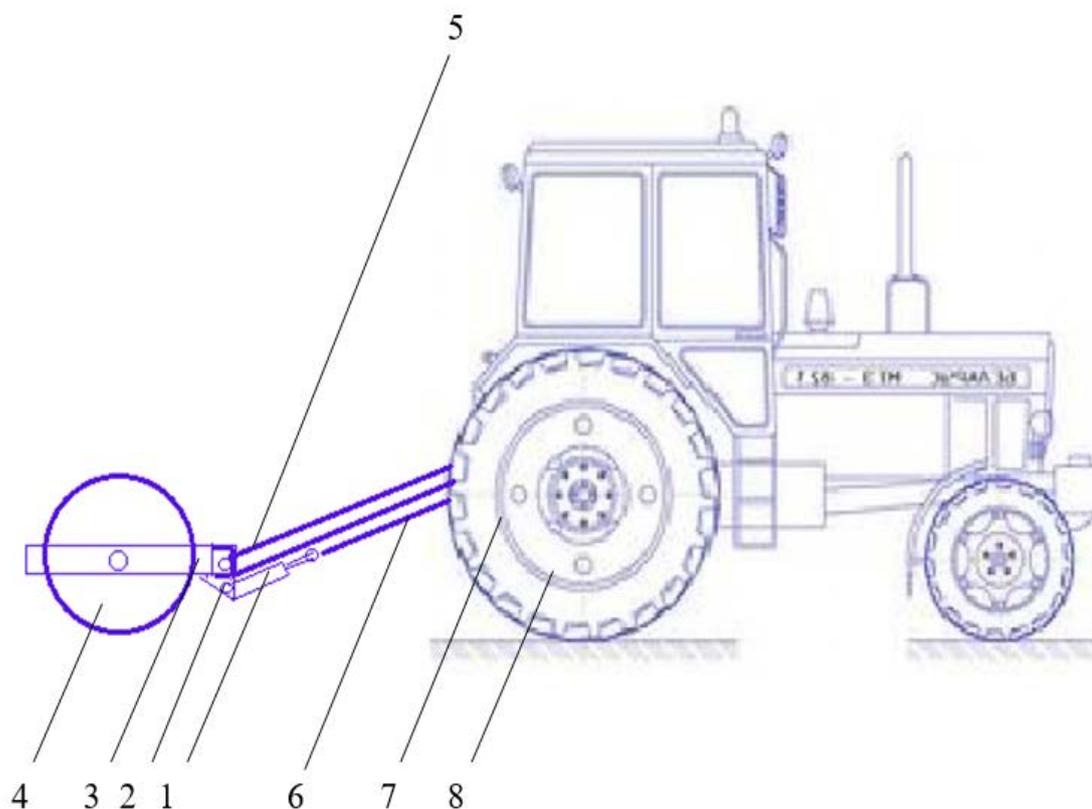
Общий вид устройства прикатывающего агрегата с установленным догружающим устройством: 1- гидроцилиндр; 2 - опорный кронштейн; 3 - рама катка; 4 - каток; 5 - сница; 6 - гибкая тросовая связь; 7- крепёжный кронштейн; 8 - трактор
